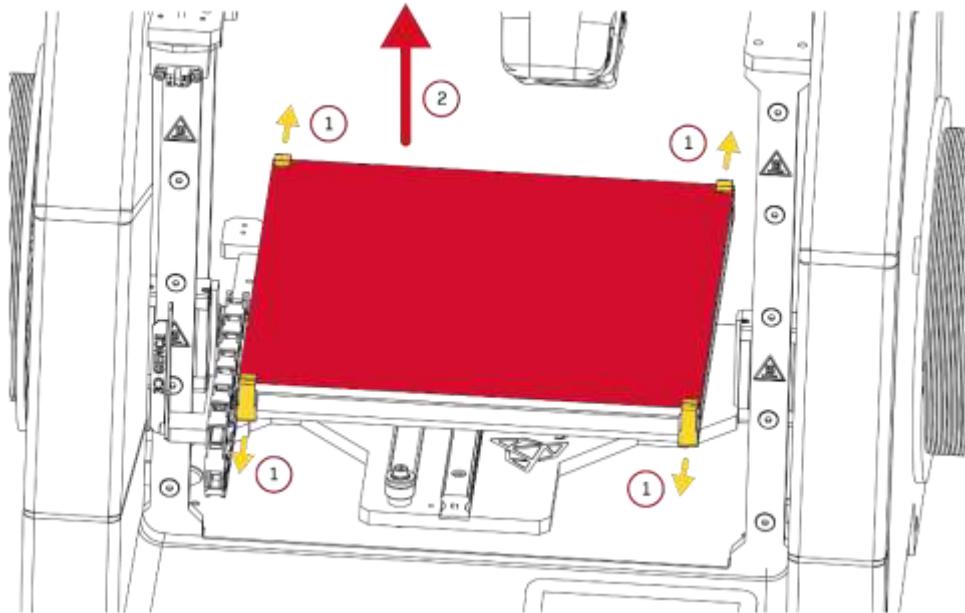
Нагревательный стол: 1. Клипсы / 2. Керамическая поверхность нагревательного стола
